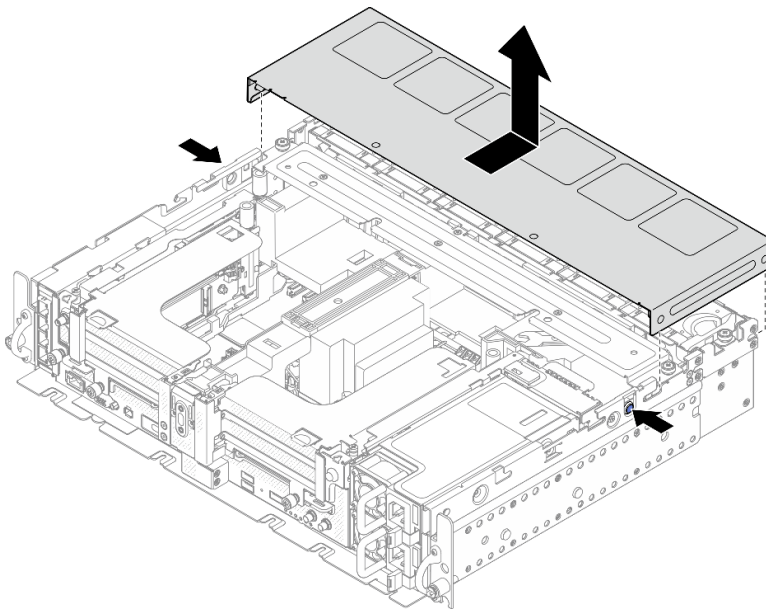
Extracción de la cubierta del ventilador (360 mm)
